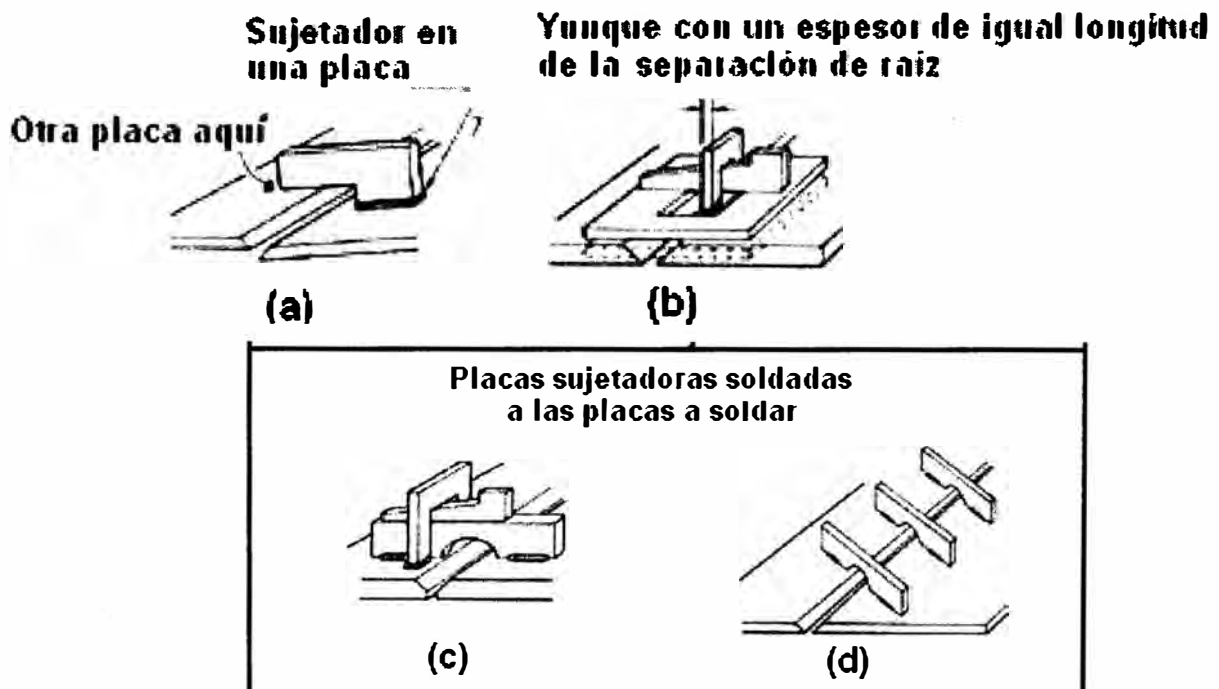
sujetadores para soldaduras a tope.
